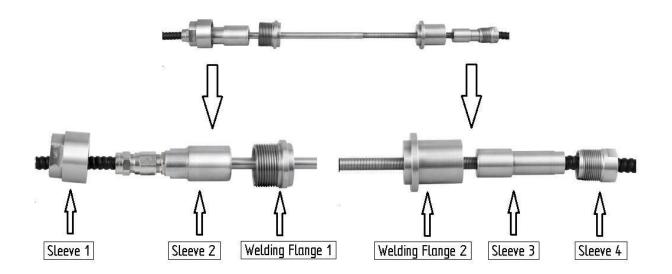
Componentes del sensor de humedad PCE-MWM 240B
